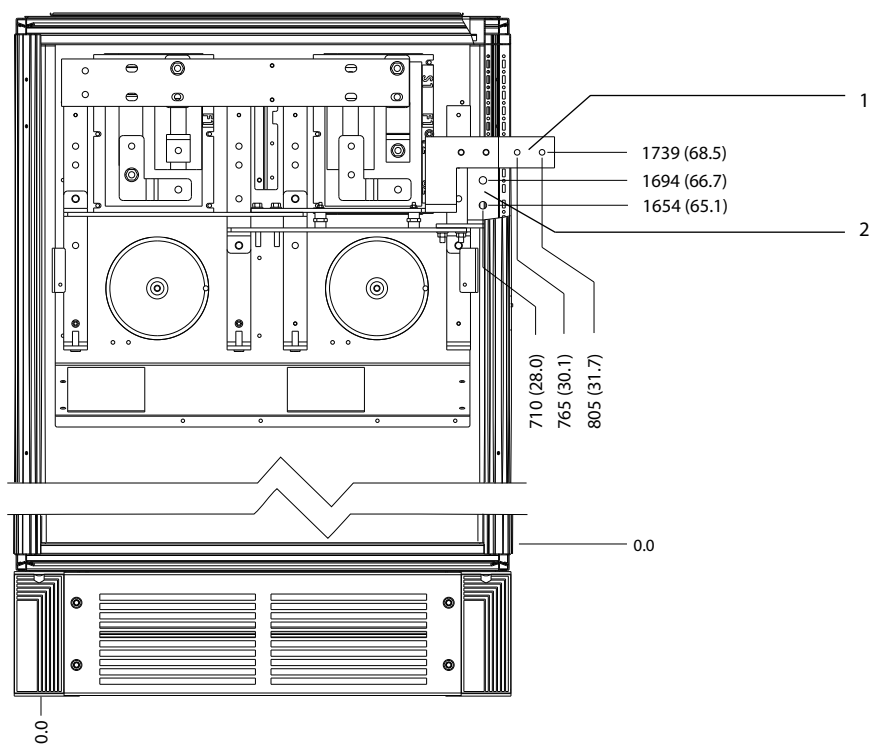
Размеры клемм для шкафа инвертора F1/F3, вид спереди
